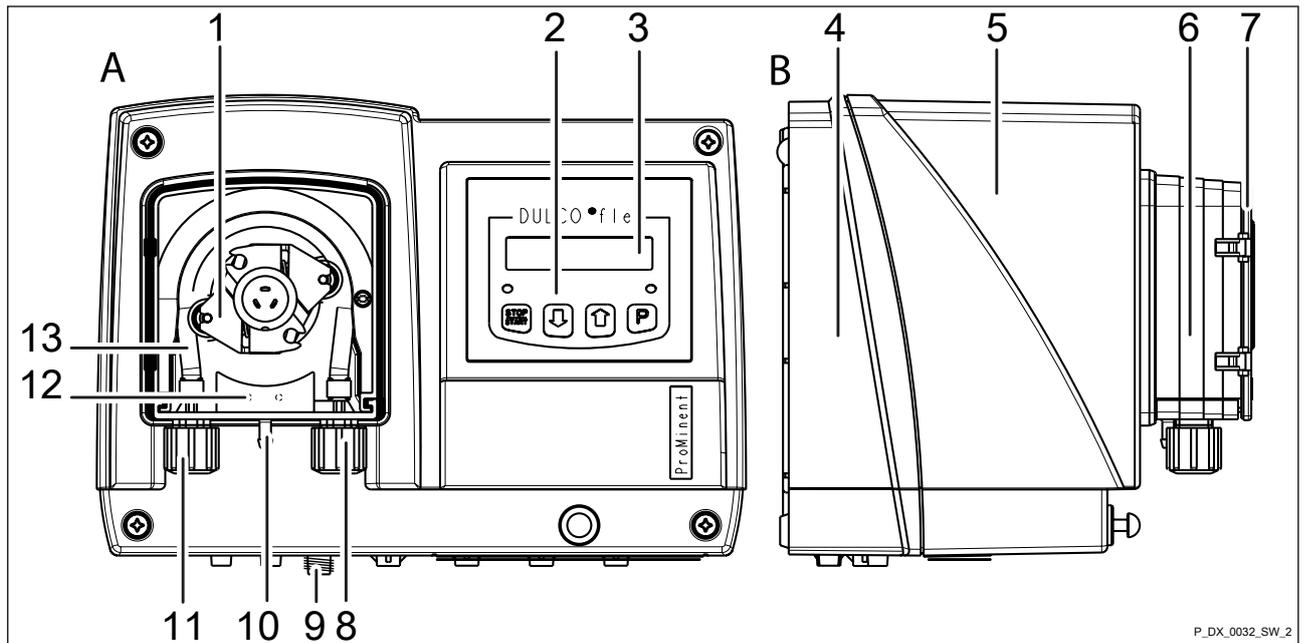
Geräteübersicht DF4a. A) Frontansicht, B) Seitenansicht / Funktionsstecker zu Buchse "Niveau"
